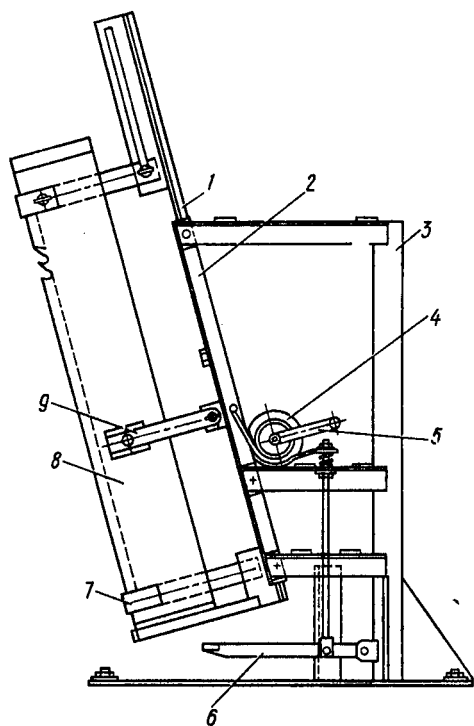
Приспособление И-50 для наплавки зубьев рамных пил стеллитом:
